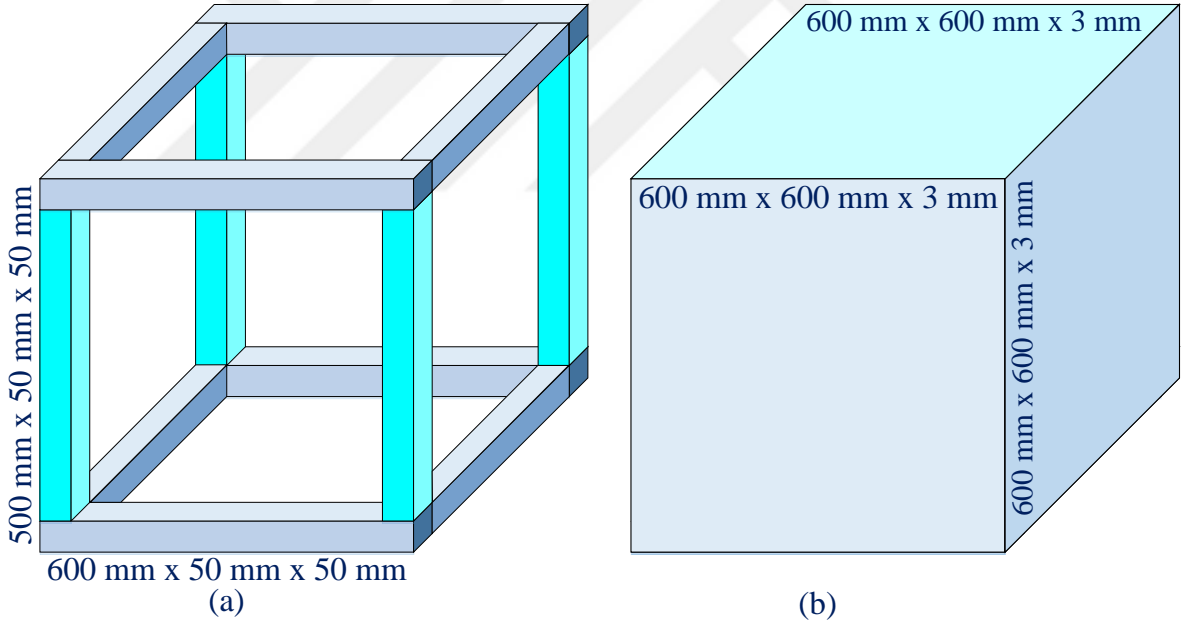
Üç boyutlu ısıtma yapan elektrik fırının blok şeması
